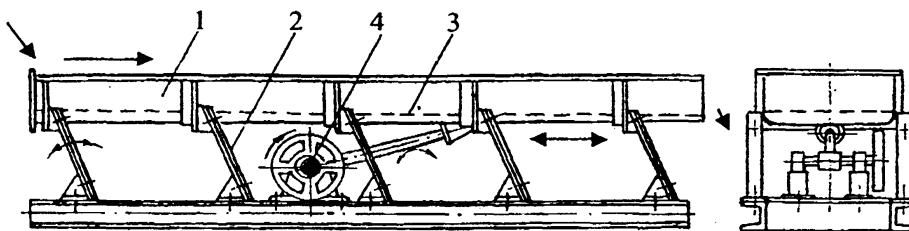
Плоский хитний грохот: 1 – прямокутний короб; 2 – листові пружини; 3 – решітка; 4 – ексцентрований вал
